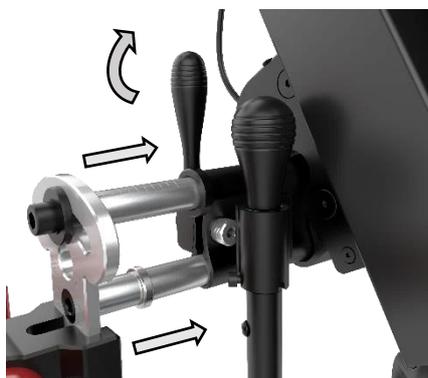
Fixation de l'ensemble de montage de la pince à l'ensemble de montage du réglage de la largeur
